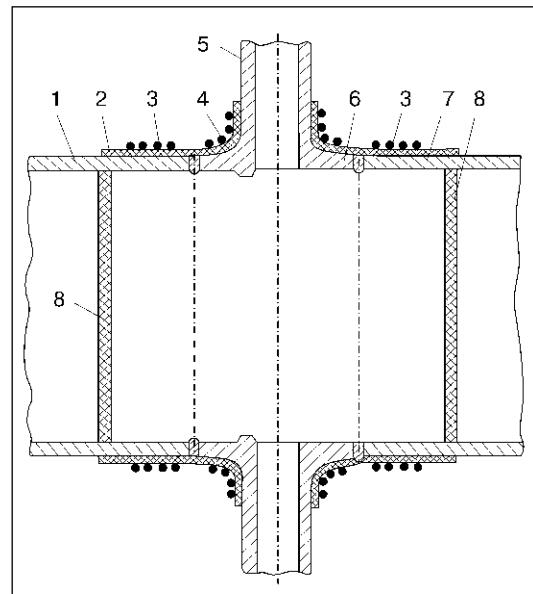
Схема установки индукторов и теплоизоляции при проведении термической обработки сварных соединений дроссельно-регулирующих клапанов: 1 — патрубок обратного клапана; 2 — наружная теплоизоляция; 3 — секция индуктора, установленная на патрубок обратного клапана; 4 — секция индуктора, установленная на штуцер дроссельно-регулирующего клапана; 5 — штуцер дроссельно-регулирующего клапана; 6 — корпус дроссельно-регулирующего клапана; 7 — переходный патрубок трубопровода; 8 — внутренняя теплоизоляционная перегородка
